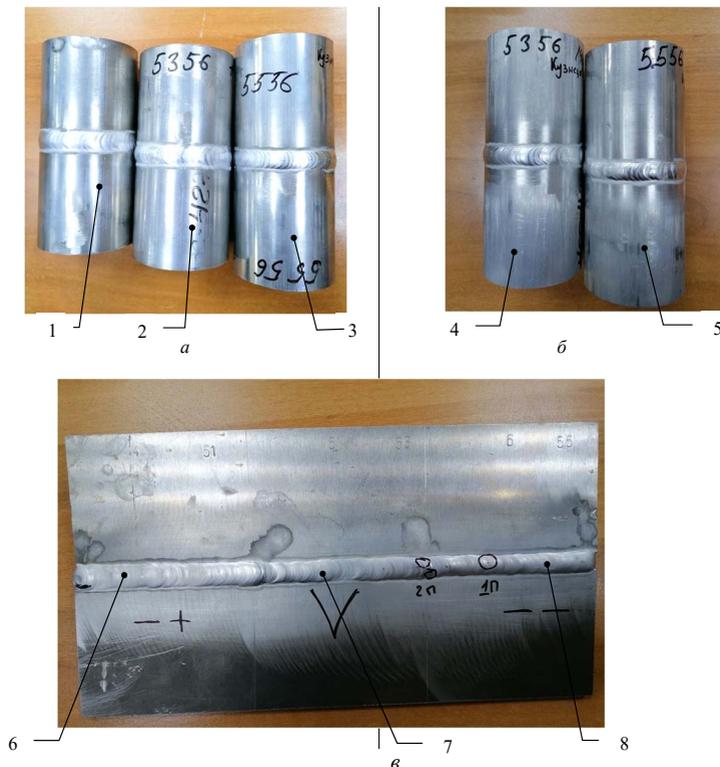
Образцы сварные, выполненные сварщиком № 2:
